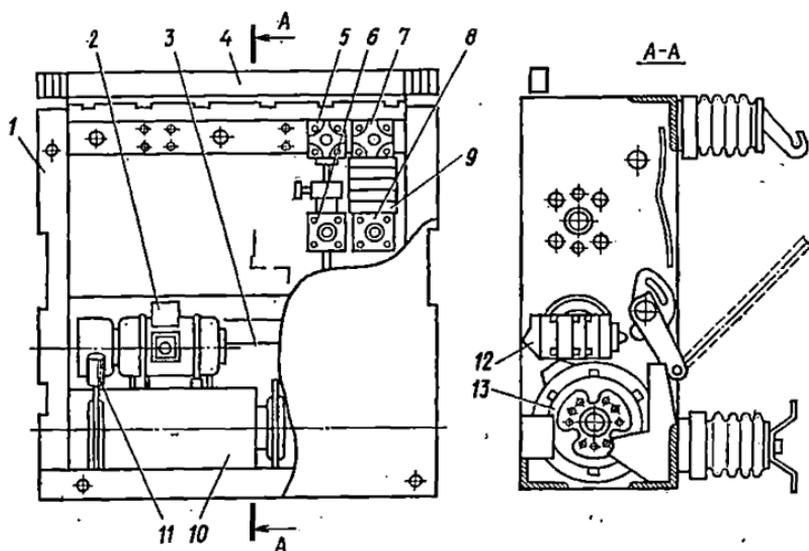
Привод, встроенный в выключатель ВМПП-10: 1 — рама, 2 — заводное устройство, 3 — вал выключателя, 4 — релейный вал, 5 и 7 — электромагниты, 6 — кнопка «откл», 8 — кнопка «вкл», 9 — вспомогательные контакты БКП, 10 — барабан и вал привода, 11 — рычаг ручного завода пружин, 12 — вспомогательные контакты БКВ, 13 — диск
